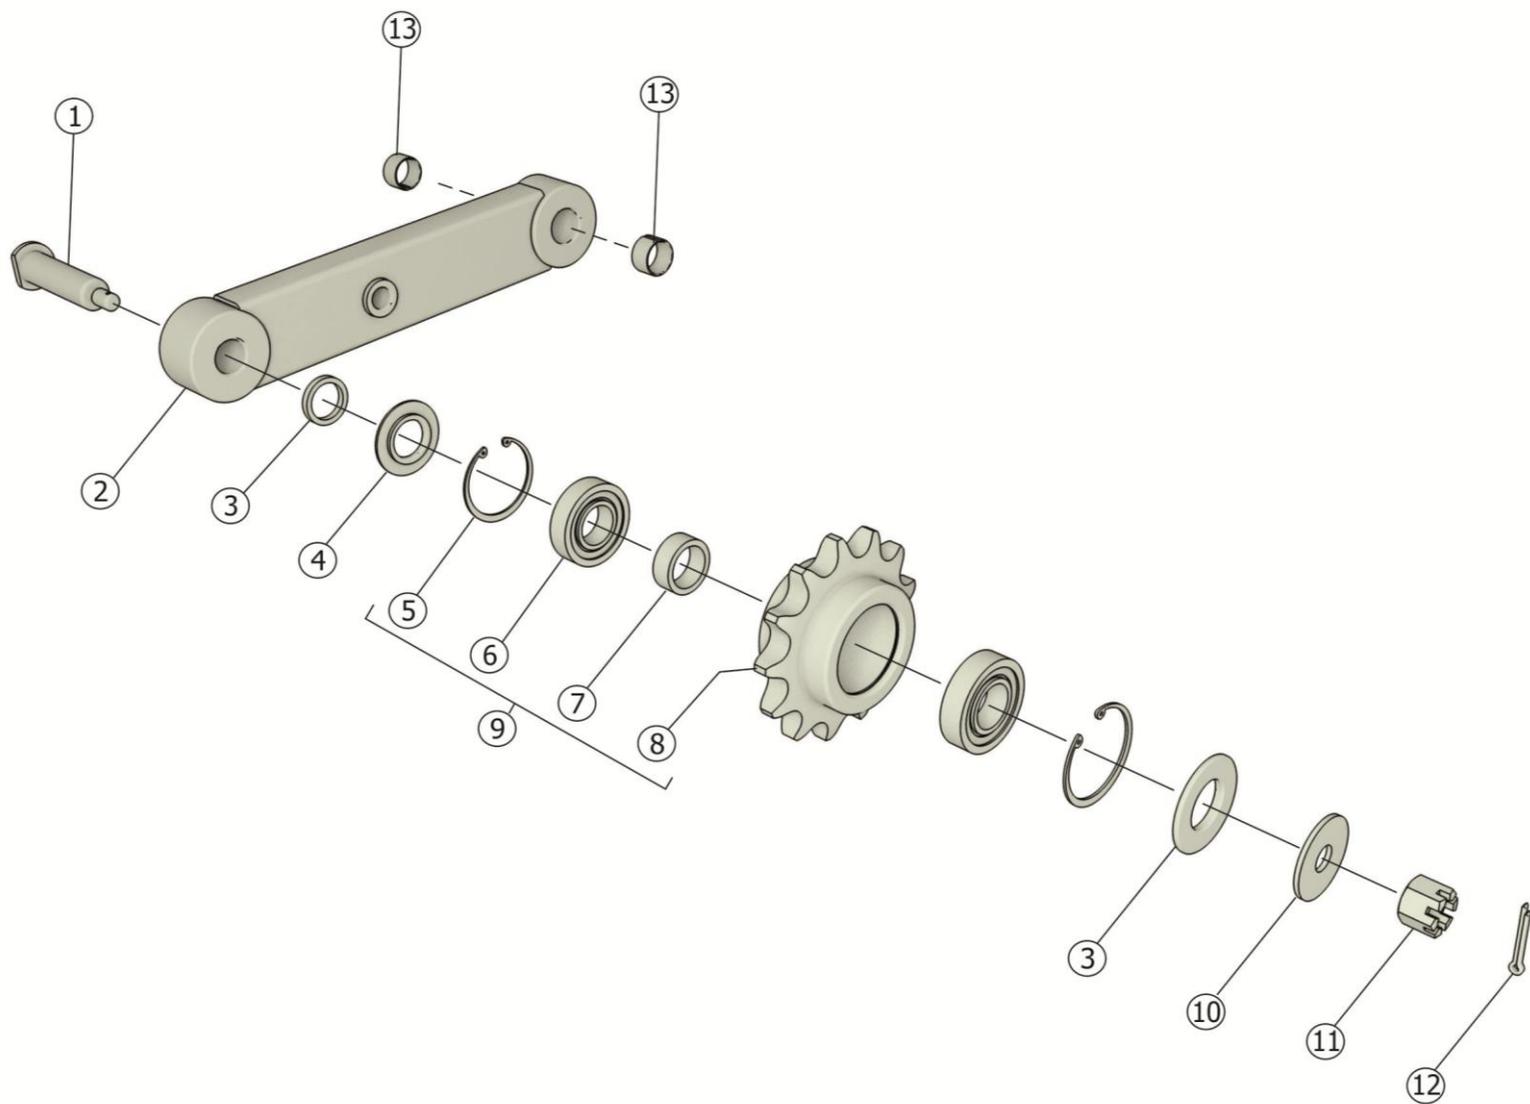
Звездочка натяжная ЖРН-604.06.00.070
